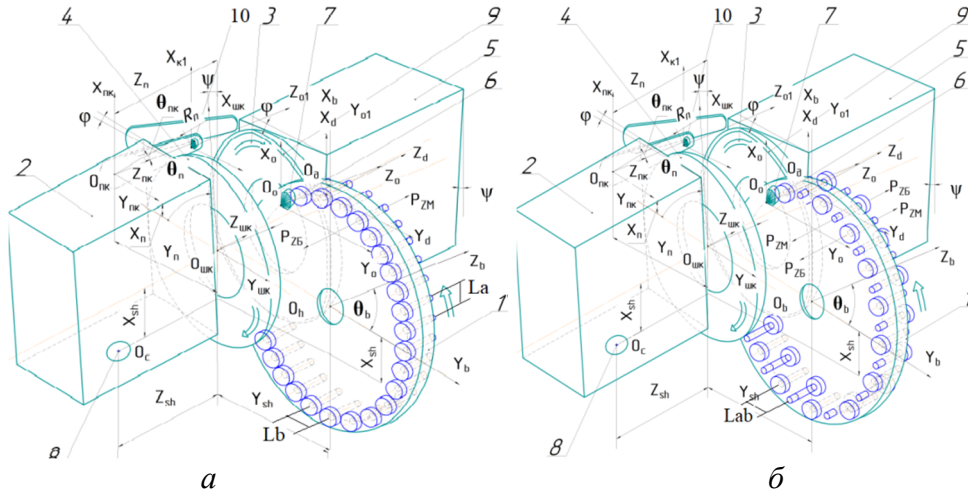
Розрахункова схема формоутворення торців деталей різних діаметрів з двома способами розташування їх у барабані подачі
